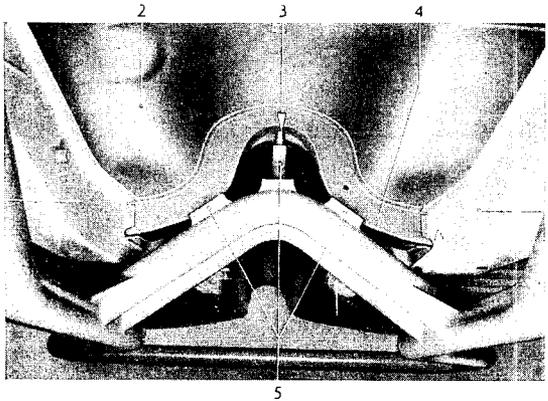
Vorderrahmenschweißlehre im hinteren Motorquerträger zentriert
